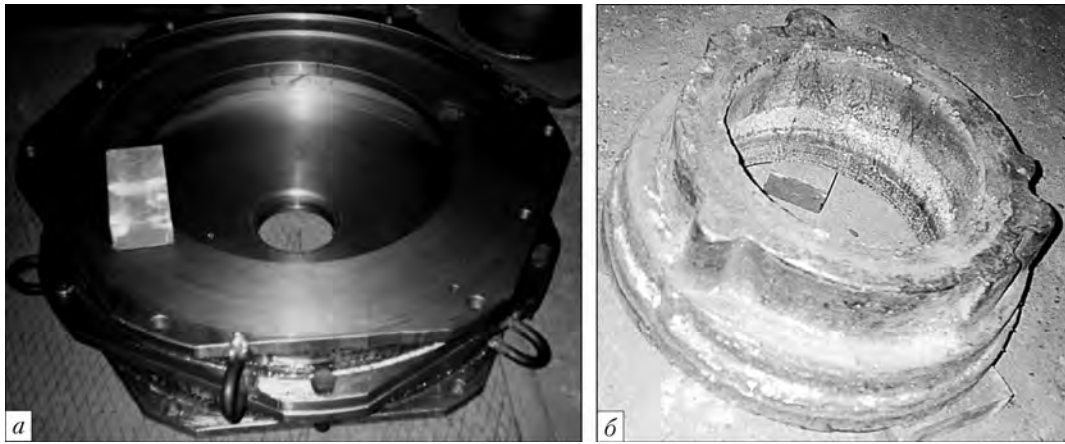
Цельный «вытряхной» одноместный кокиль ЦЭШЛ (а) и заготовка зубчатого колеса для карьерного автомобиля МАЗ (б)
